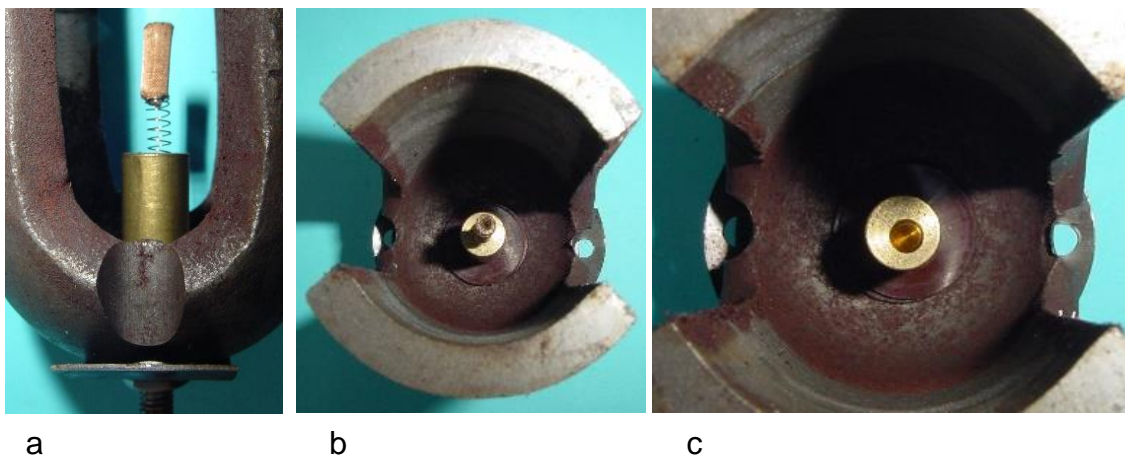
Bürstenhalter: a) Schraubenfeder mit aufgesetzter Kupfergewebebürste, b) Bohrung im Bürstenhalter
